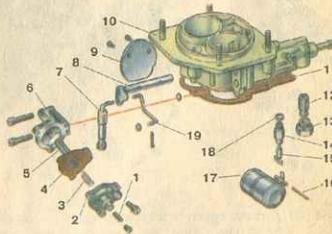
Детали крышки карбюратора: 1 — регулировочный винт; 2 — крышка пускового устройства; 3 — пружина; 4 — диафрагма; 5 — рейка диафрагмы; 6 — корпус пускового устройства; 7 — телескопическая тяга; 8 — ось воздушной заслонки; 10 — крышка карбюратора; 11 — прокладка; 12 — фильтр; 13 — пробка фильтра; 14 — седло игольчатого клапана; 15 — игольчатый клапан; 16 — ось поплавка; 17 — поплавок; 18 — прокладка; 19 — тяга пускового устройства
